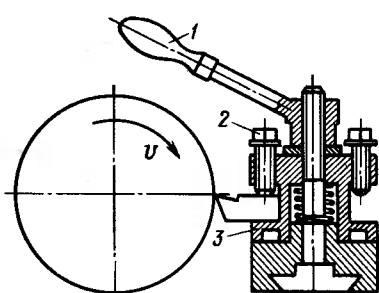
Четырехпозиционный резцедержатель токарного станка и установка инструмента в нем
